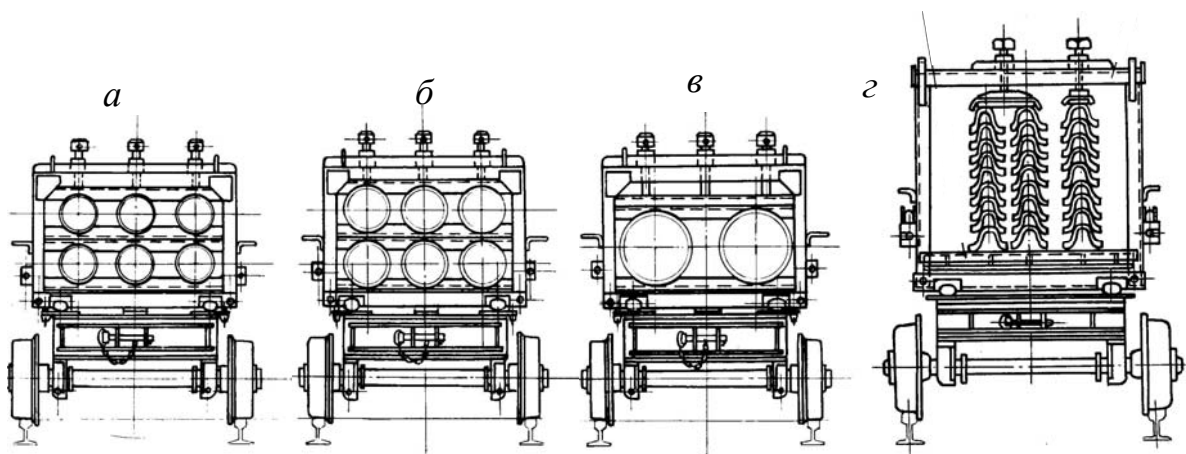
Схеми розміщення труб та аркового кріплення на устаткуванні УДГ:
